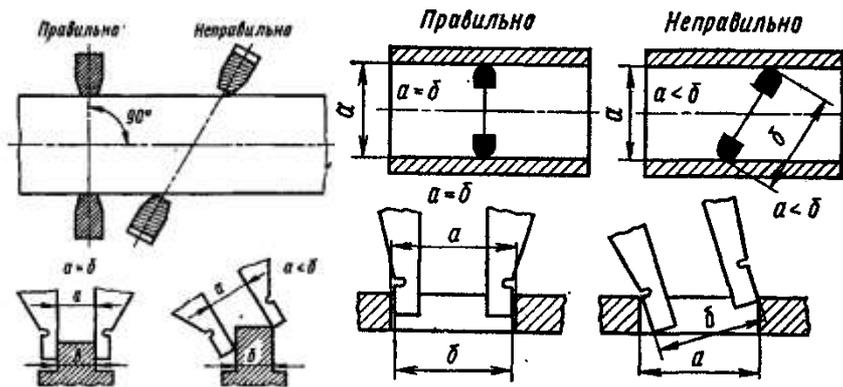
Установка штангенциркуля при измерении наружных поверхностей
